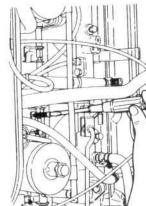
Desserrage de la vis de réglage d'équilibrage ET212
